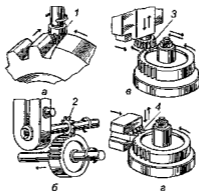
Нарезание зубчатых колес копированием с помощью фрез и обкаткой с помощью долбяка и гребенки: 1 – пальцевая фреза; 2 – модульная дисковая фреза; 3 – долбяк; 4 – гребенка
